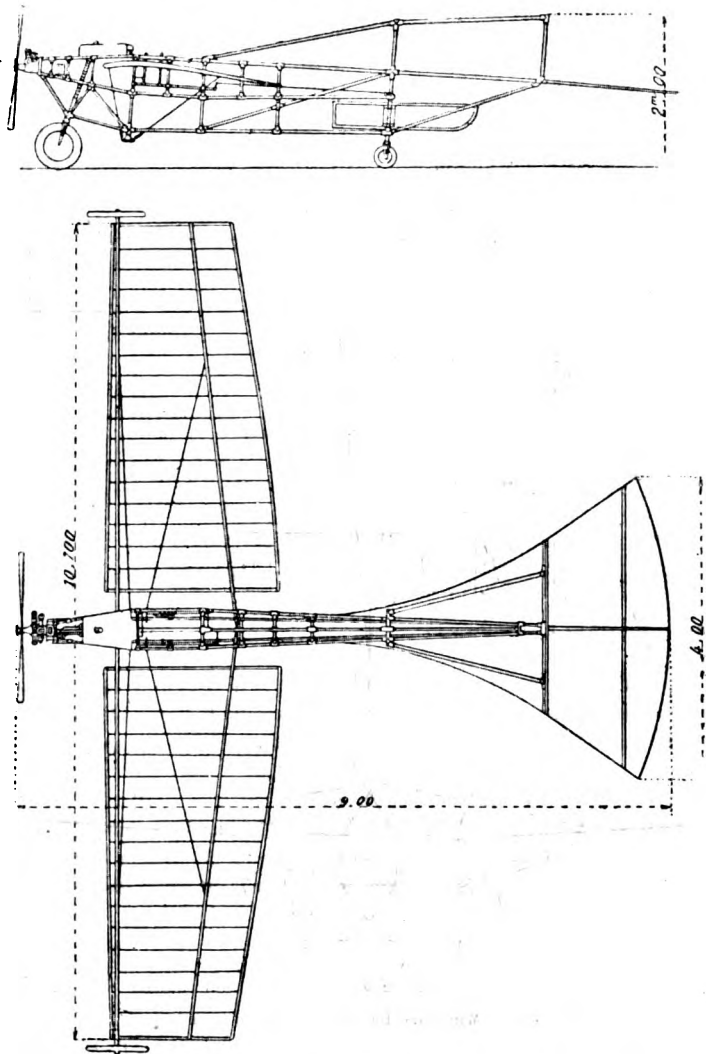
Monoplano R. Esnault-Pelterie - Pianta e sezione.
